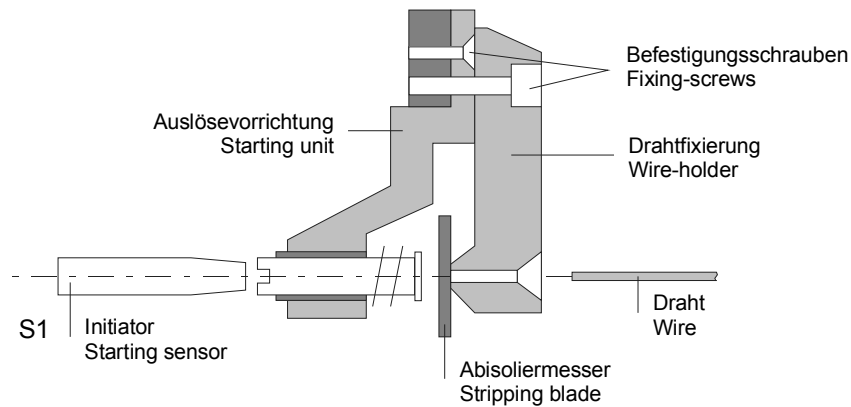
Drahtfixierung und Auslösevorrichtung / Wire holder and Starting unit
